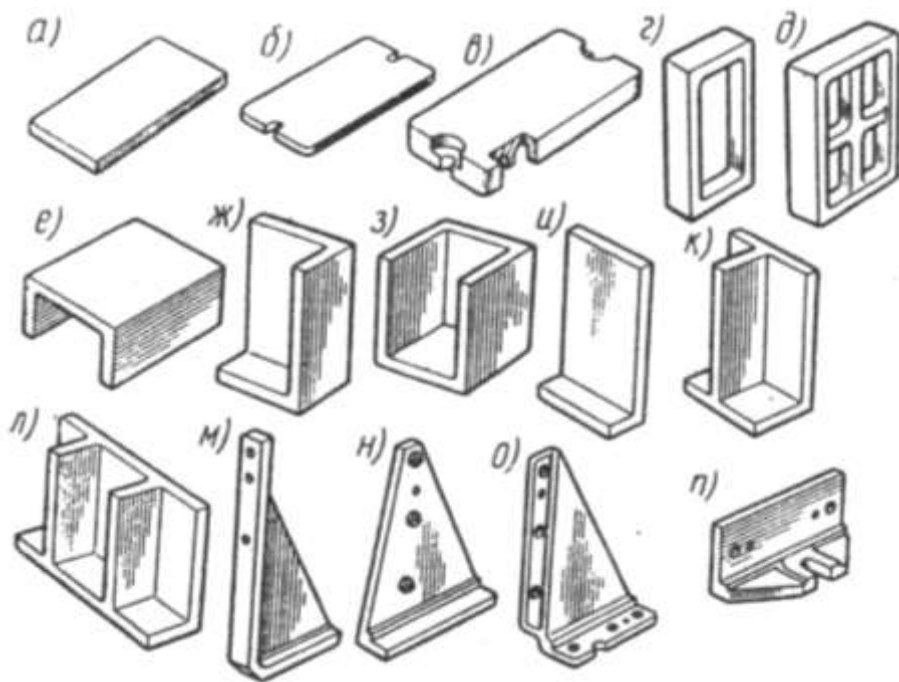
Типы нормализованных элементов корпусов: а — плиты стальные; б-в — плиты чугунные; г-д — коробки; е — швеллеры; ж — трехгранник; з — четырехгранник; и — угольники; к-л — угольники с ребрами; м-о — ребра; п — планки
